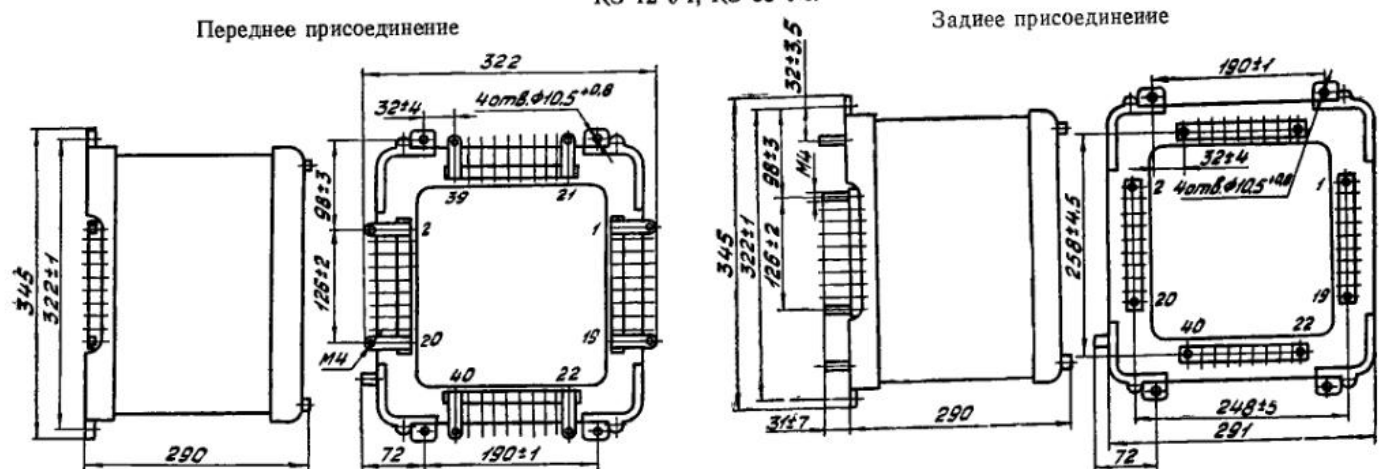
Габаритные, установочные, присоединительные размеры комплектов защиты типов КЗ 13 У4, КЗ 17 У4, КЗ 36 У4.
